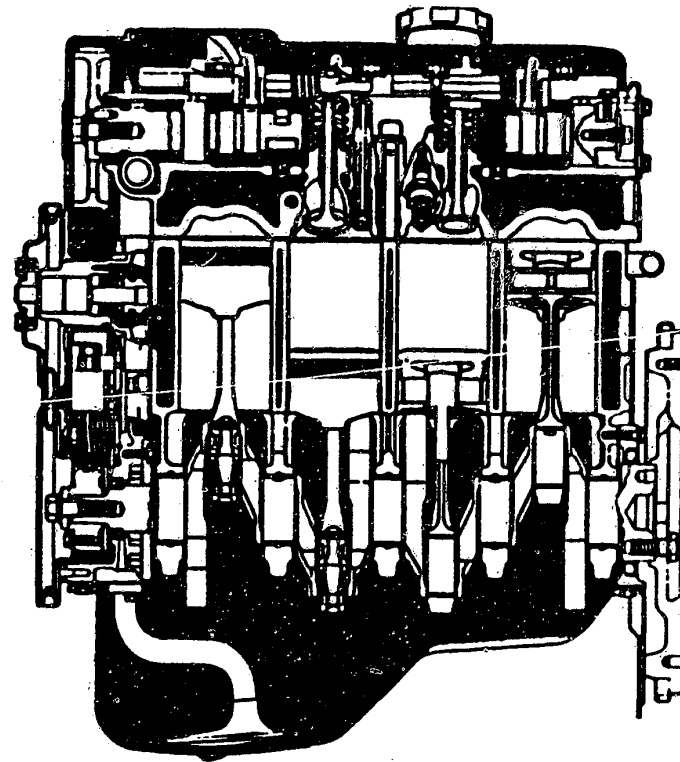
Längsschnitt durch den 4G1-Motor mit oberliegender Nockenwelle.
